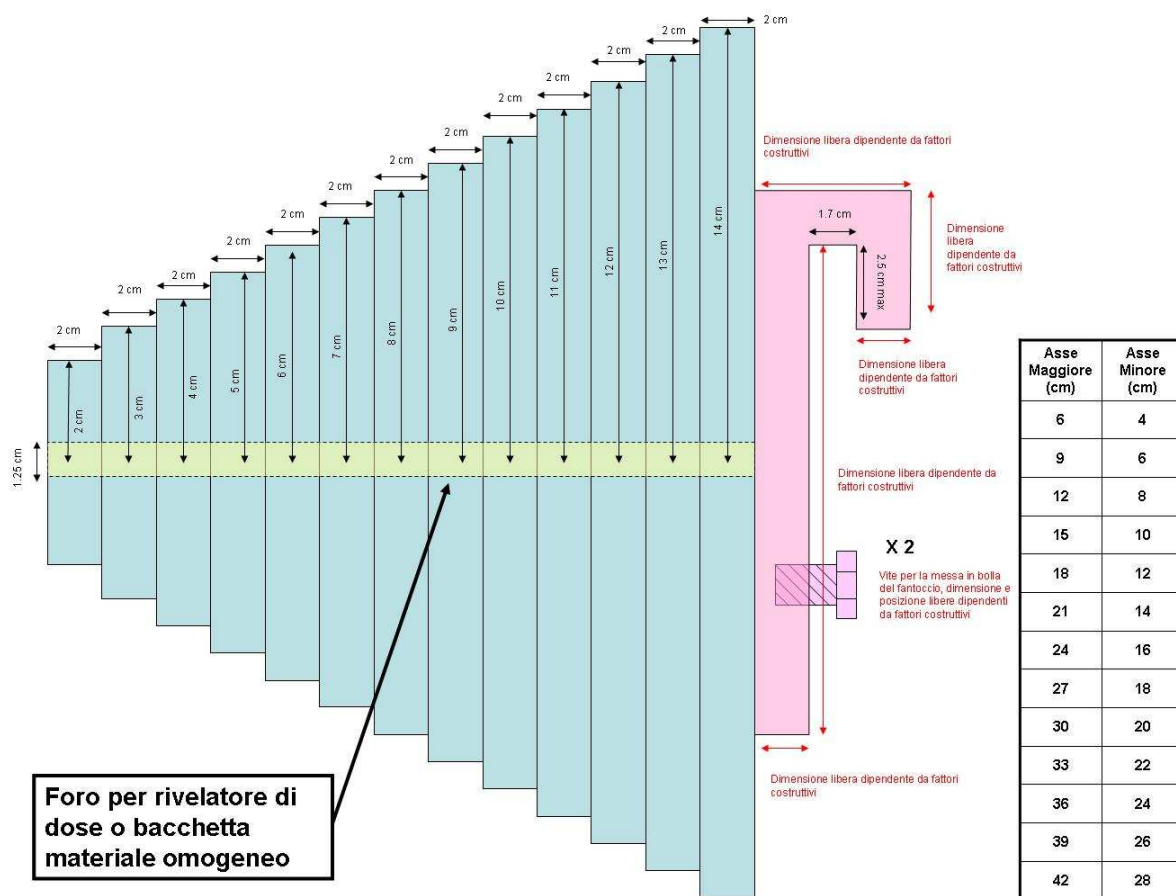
Sezione longitudinale dell'oggetto test DOSE AUTOMATICA CONO
